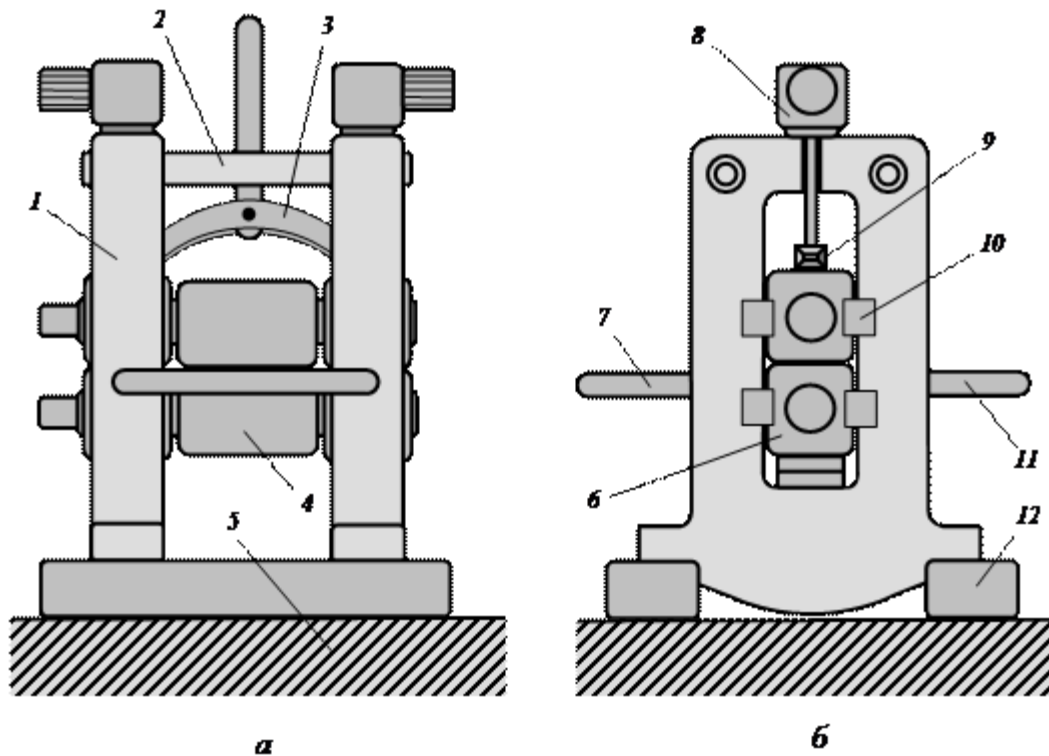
Схема робочої кліті прокатного стану: *a* – вигляд з переду; *б* – вигляд збоку; *1* – станина; *2* – траверса; *3* – урівноважуваче устаткування; *4* – робочі валки; *5* – фундамент; *6* – подушка; *7, 11* – лінійки; *8* – натискний механізм; *9* – устаткування для запобігання переміщення; *10* – механізм встановлення та фіксації прокатних валків; *12* – щитовина
